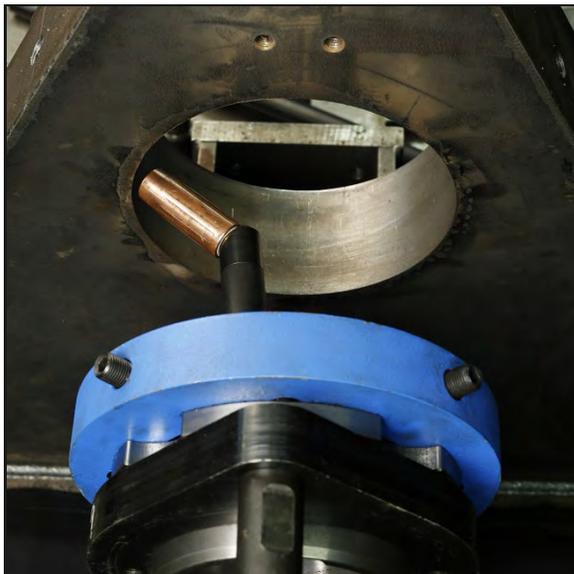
BALANCEO DE LA MÁQUINA DE SOLDADURA DE PERFORACIÓN PARA ALCANZAR EL CENTRO
